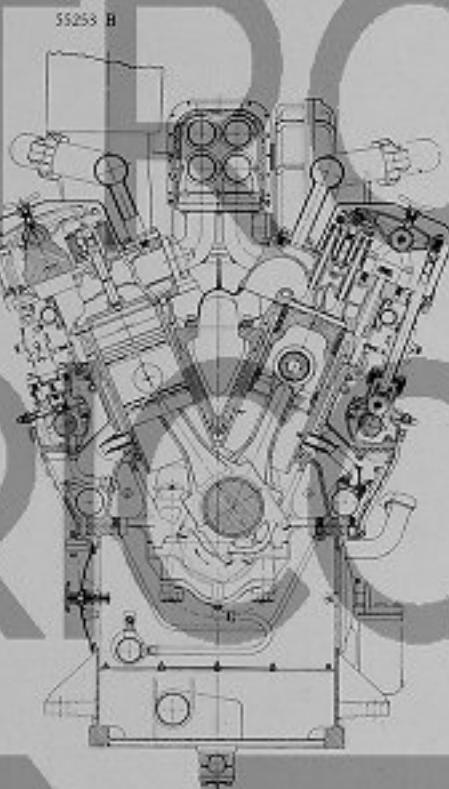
Sezione trasversale del motore ALCO tipo 244
